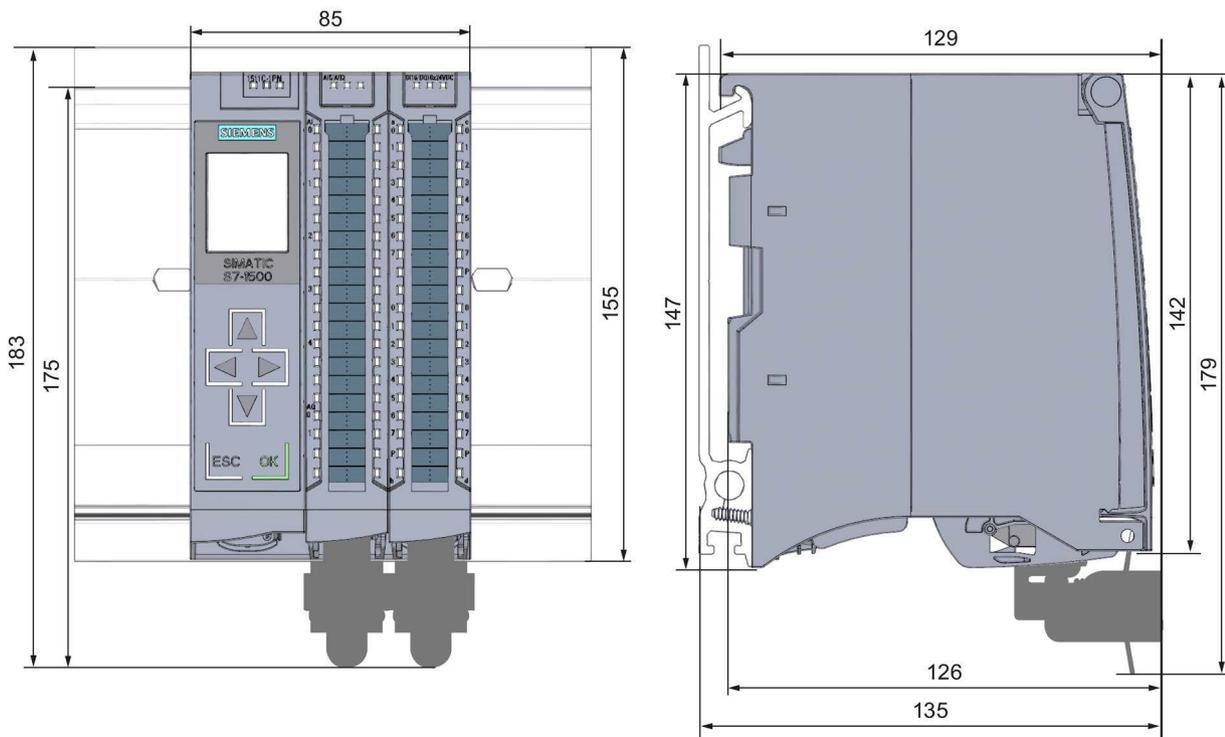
Dessin coté de la CPU 1511C-1 PN , vue de face et de côté
